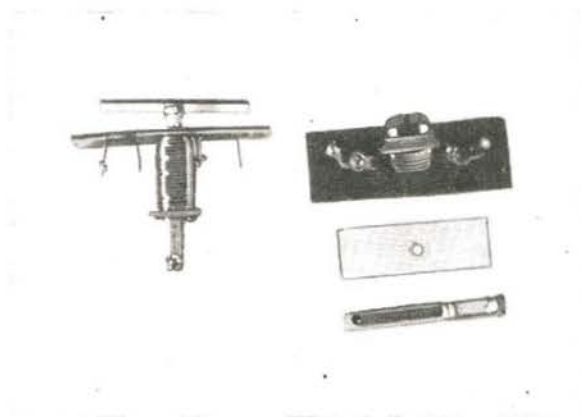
Entkuppler: links Seitenansicht komplett, rechts oben Draufsicht, darunter Pertinaxplatte und Hubkern
